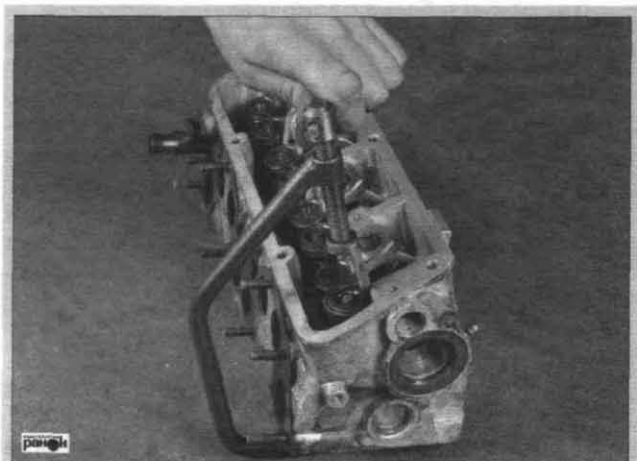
Сжатие клапанных пружин при помощи приспособления
